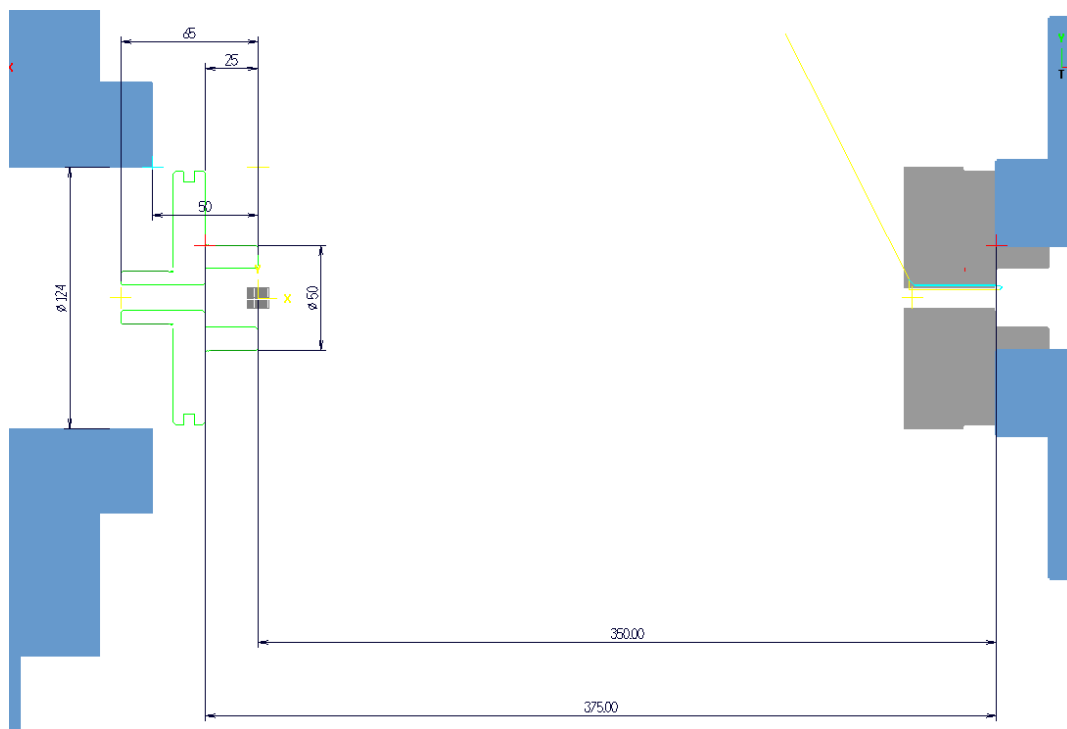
Předání obrobku pomocí příkazu „*Dráhy nástrojů/ Různé/ Předání obrobku*“
